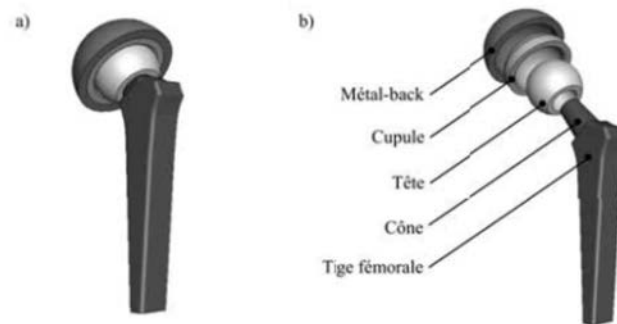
Prothèse totale de hanche (PTH) a) vue assemblée b) vue éclatée (Hausselle 2007)
